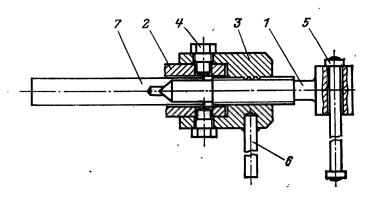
Съеминк для снятия двигателей АРК с ролнка рольганга. 1— винт; 2— вал двигателя; 3— гайка; 4— болт; 5— рукоятка; 6— штифт; 7— стержень.
